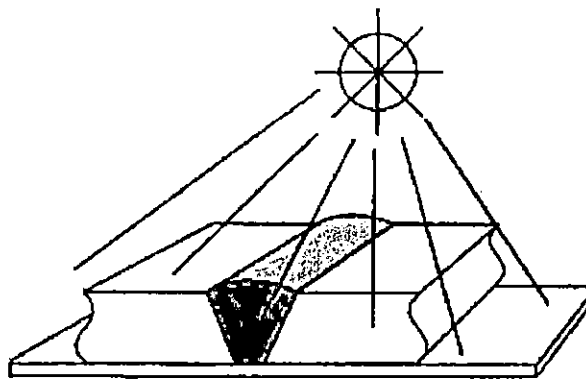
En la figura se ha representado una soldadura la cual esta siendo expuesta a una fuente radiológica para realizar su inspección La fuente radiológica puede tratarse de una fuente de partículas alfa, beta o neutrones, o bien rayos X ó gamma, las más populares son las últimas dos. ^[1-48]
